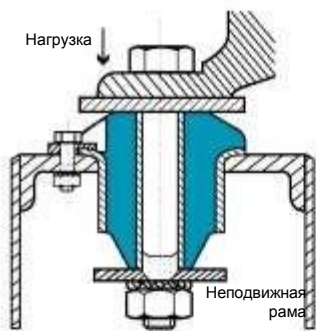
Установка между оборудованием и металлической рамой (безотказная работа для мобильного оборудования).
